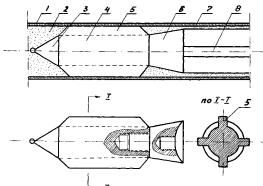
Схема пристосування для нанесення катализатора на внутрішню поверхню труб:
